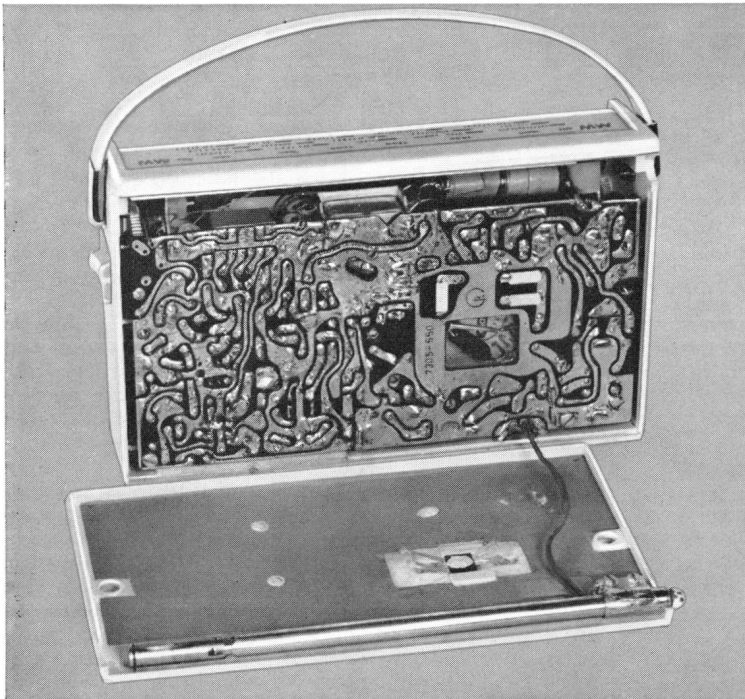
Blick auf die gedruckte Schaltung des prima-boy
